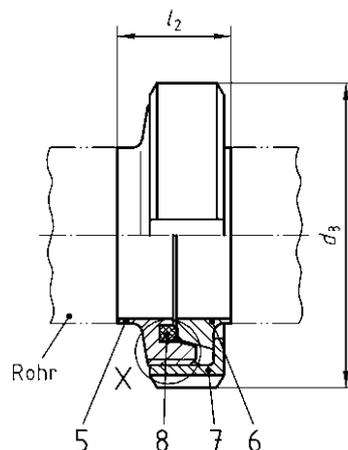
Rohrverschraubung zum Stumpfschweißen
